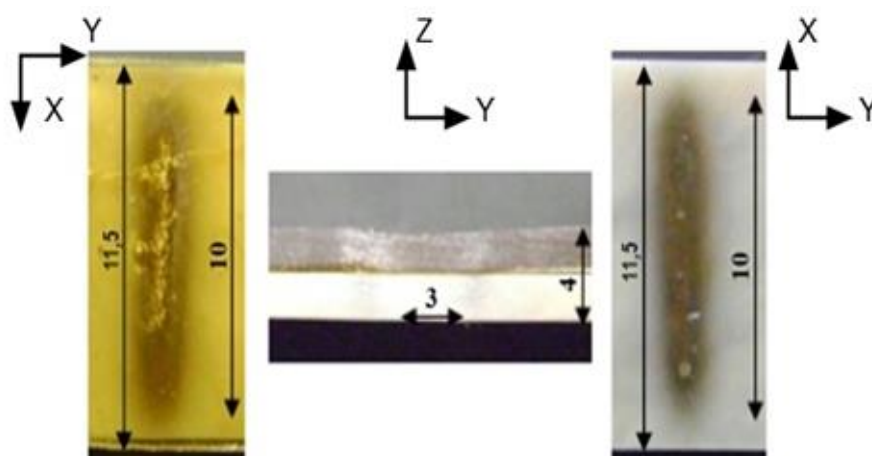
Assemblage soudé à  $24 \text{ J.mm}^{-2}$ . A gauche : vue de dessus, au centre : vue latérale, à droite : vue de dessous. Les dimensions sont exprimées en mm
